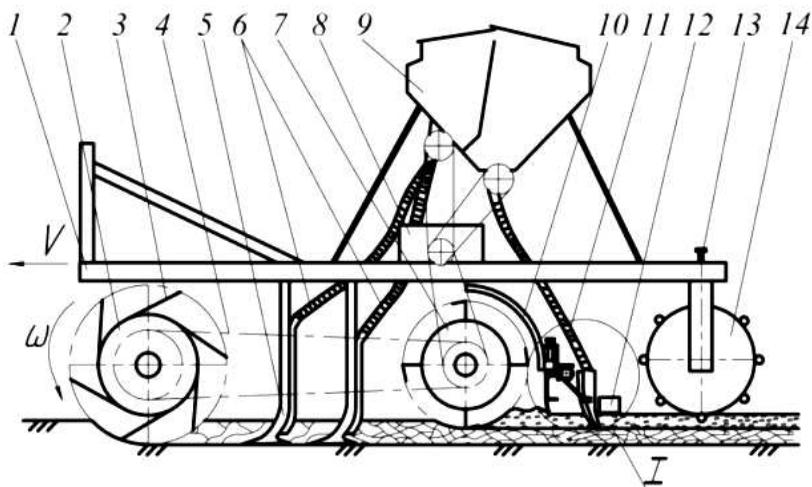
Агрегат для предпосевной уборки почвы и посева (вид сбоку)
